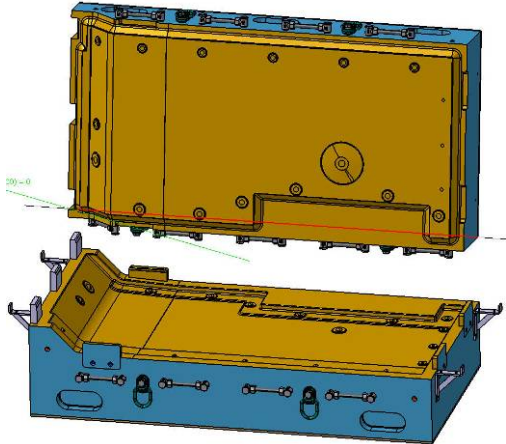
Werkzeug Bodenplatte 4 (CAD)
